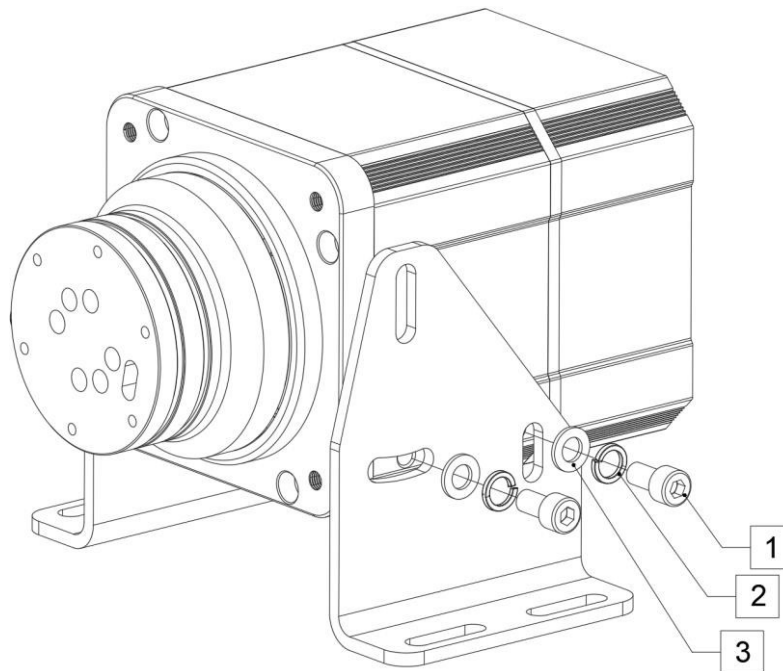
Montage des VNM-Radstands Premier, Elite, Supreme mit seitlicher Halterung. Die Radstände Premier, Elite und Supreme werden mit 4xM8-Schrauben der Länge 20 mm mit 1,25 mm Gewindesteigung (1), 4xM8 Federscheiben (2) und 4xM8 Unterlegscheiben (3).
